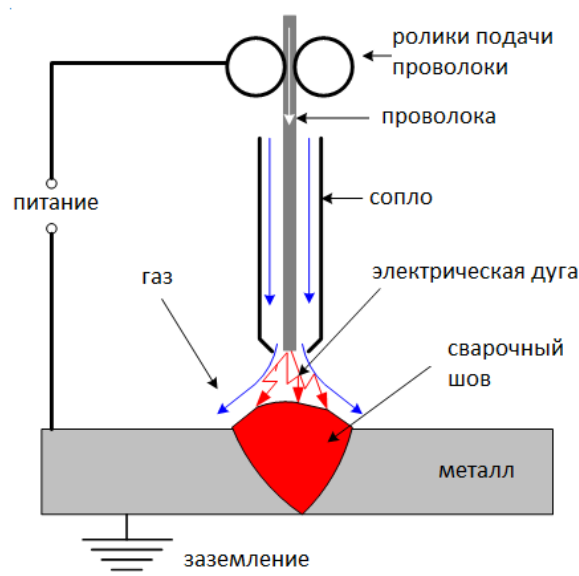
Принцип полуавтоматической сварки проволокой в газовой среде
